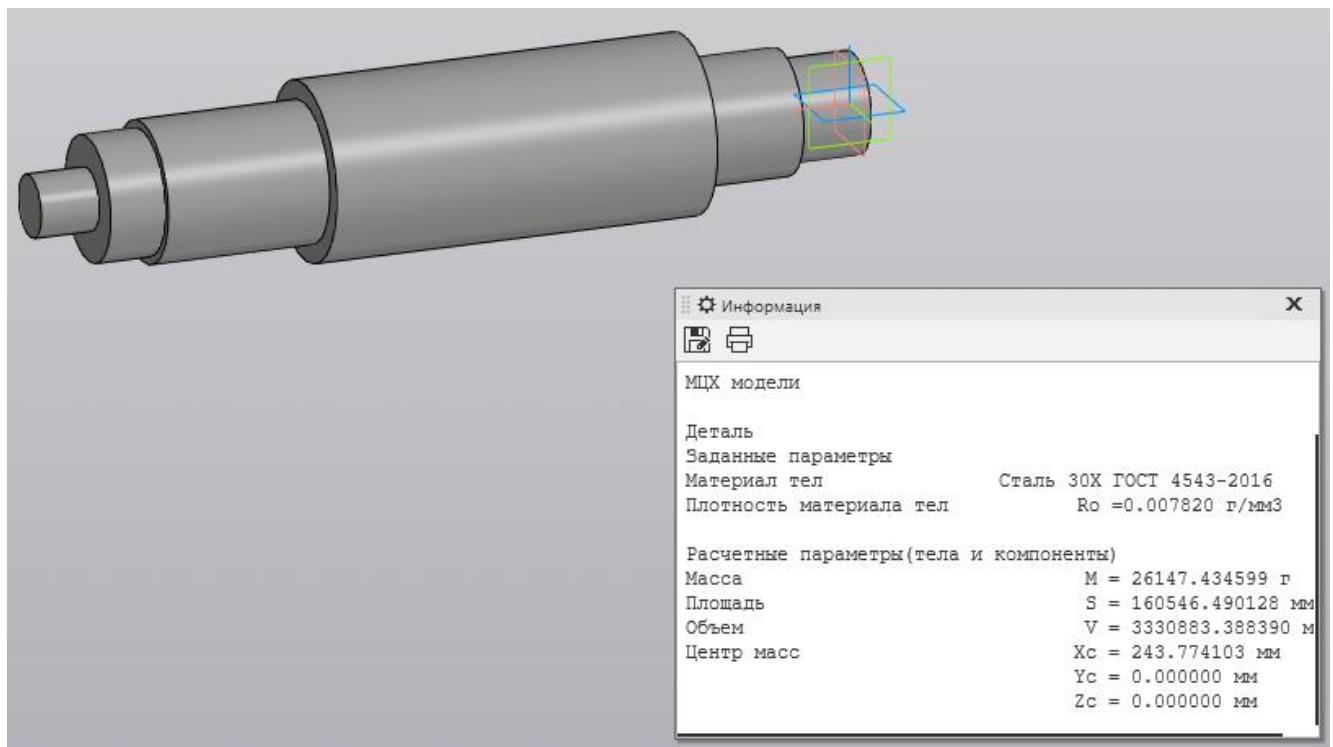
3D модель заготовки виготовленої на ГKM
